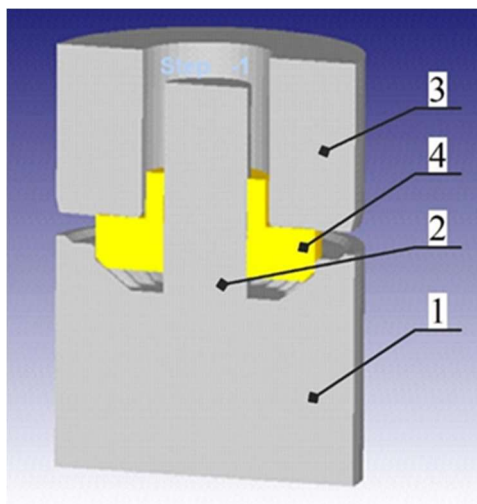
3D-модель инструмента и заготовки для штамповки конического зубчатого колеса:
